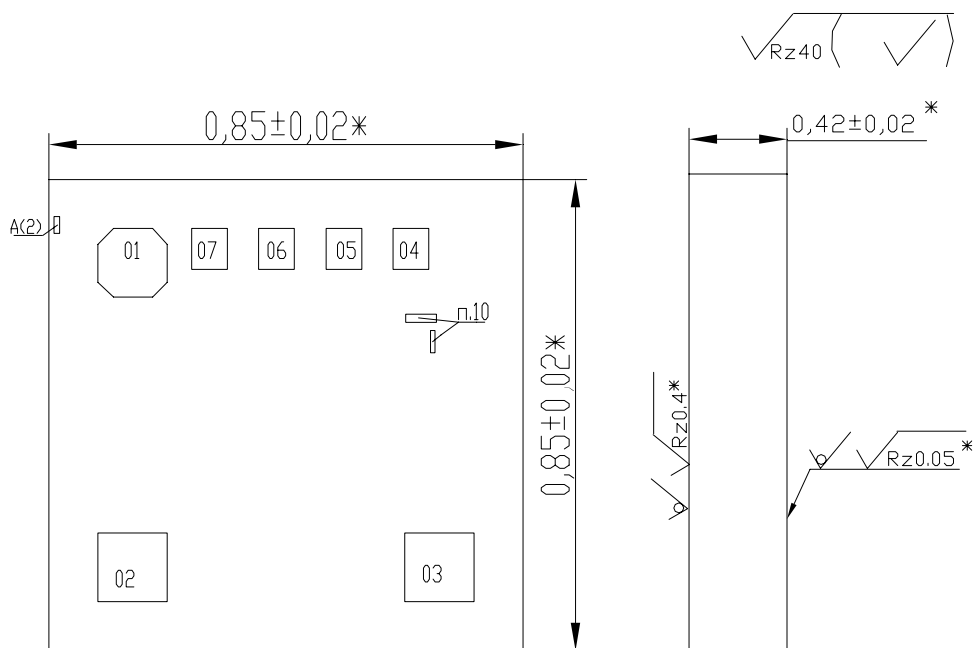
Габаритный чертеж кристалла 142EP2H4ИМ
